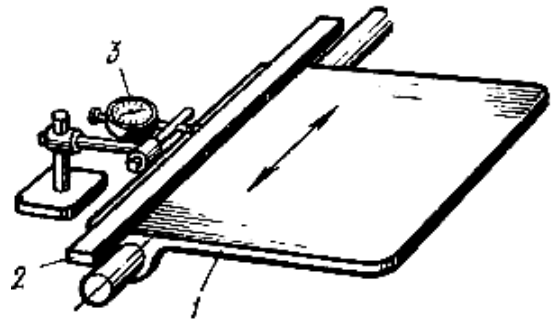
Проверка прямолинейности перемещения каретки по направляющим: 1 — каретка, 2 — поверочная линейка, 3 — индикатор
